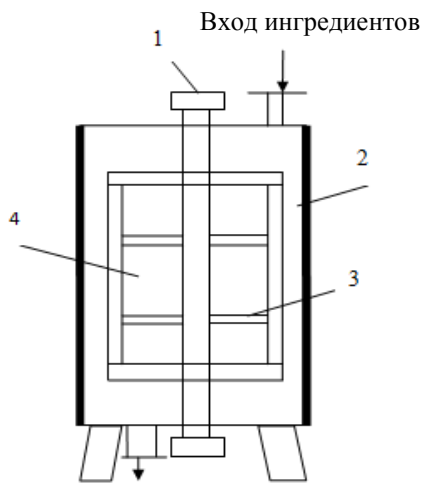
Аппарат для предварительной обработки (смешивания) жидких кормовых смесей: 1 – вал мешалки; 2 – корпус; 3 – ребра; 4 – рамная мешалка; 5 – выгрузной патрубок
